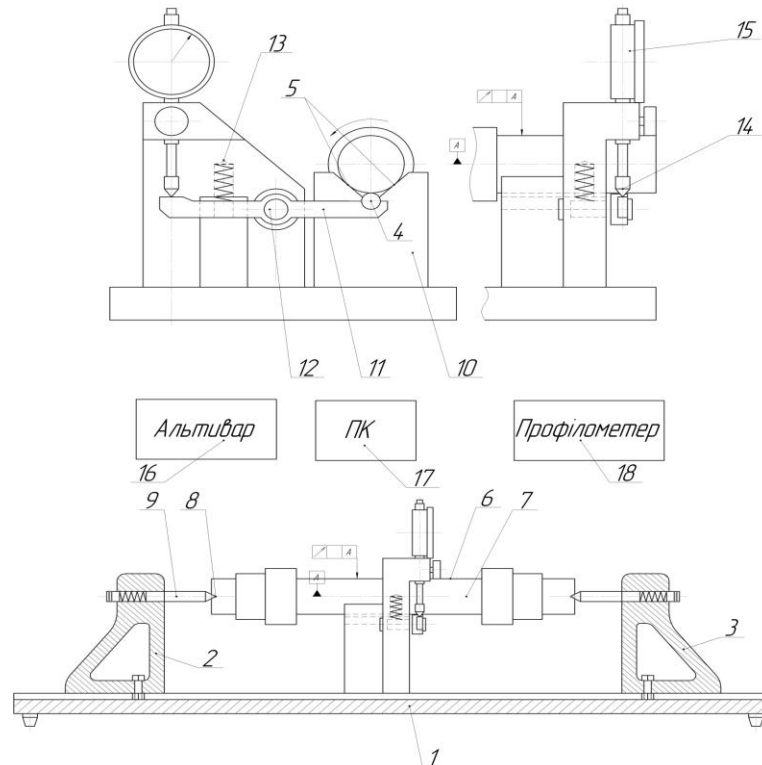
Багатомірний пристрій для контролю ступінчастих валів
